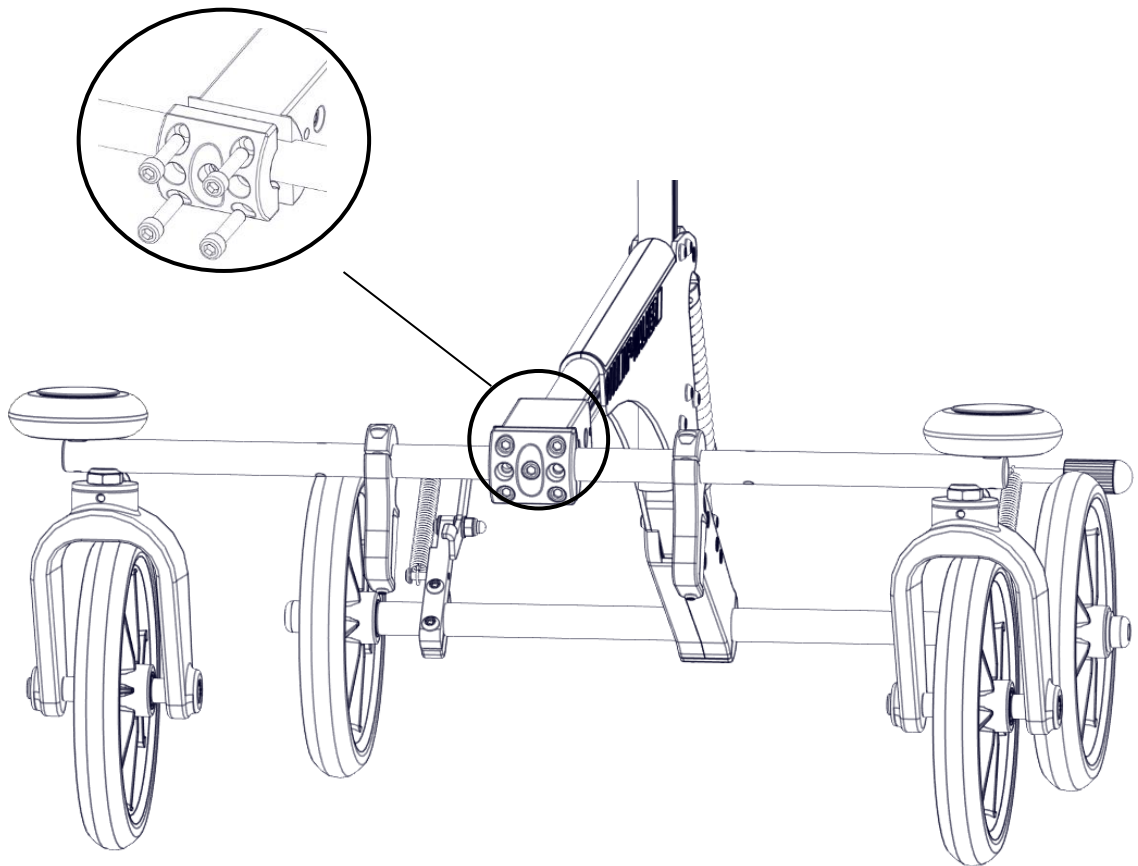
Soltando os parafusos Unbraco do eixo frontal
